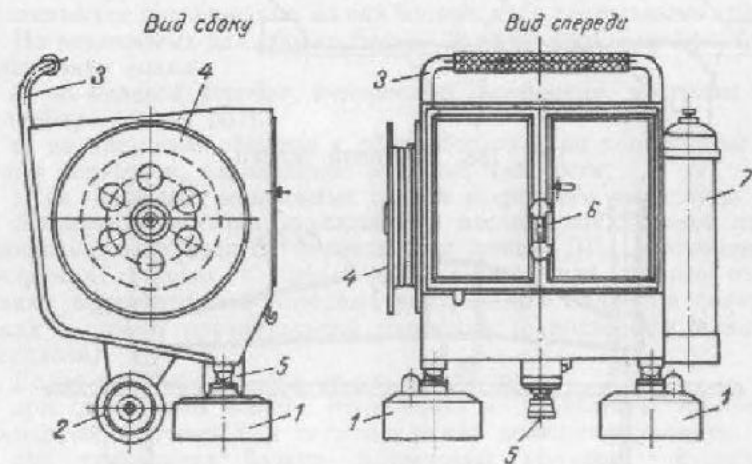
Схема приспособления с электромагнитами для стыкования обшивки в нижнем положении.
